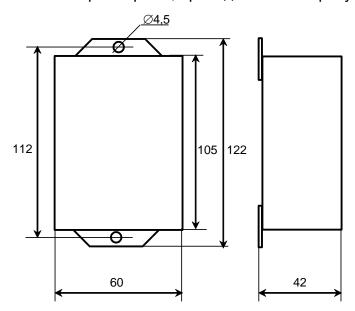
Габаритные и установочные размеры МС1218
